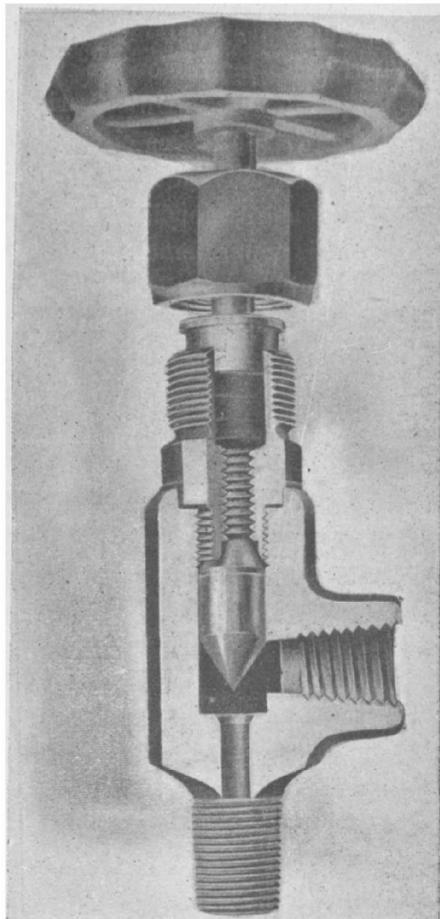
Robinet de réglage à pointe de la Buffalo Refrigerating Machine Co.
